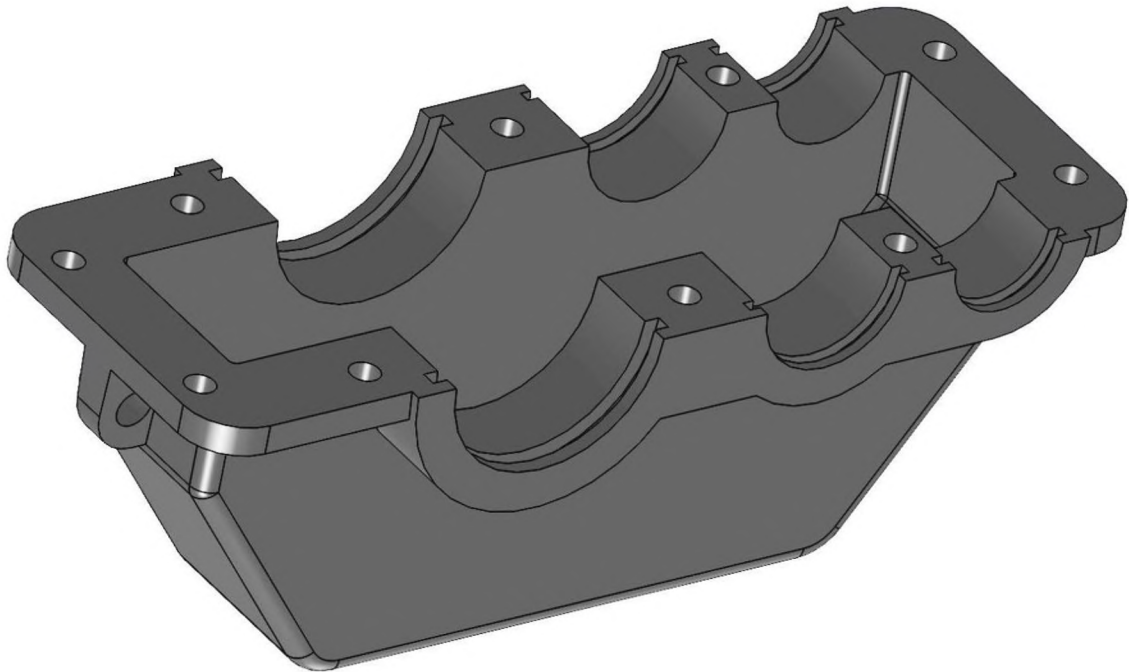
Тривимірна модель деталі «Корпус»
